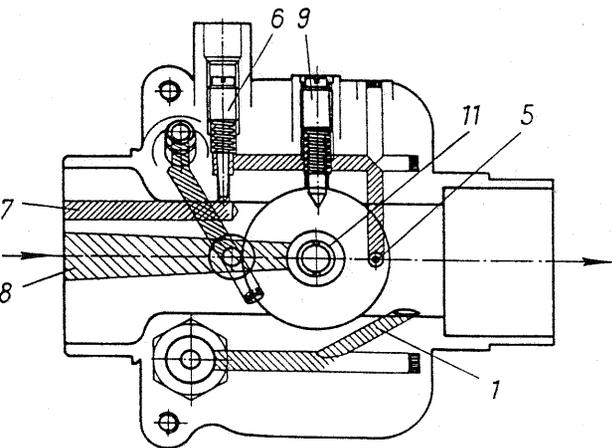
Carburateur BVF 22 ... 24 N 2 en vue de coupe
